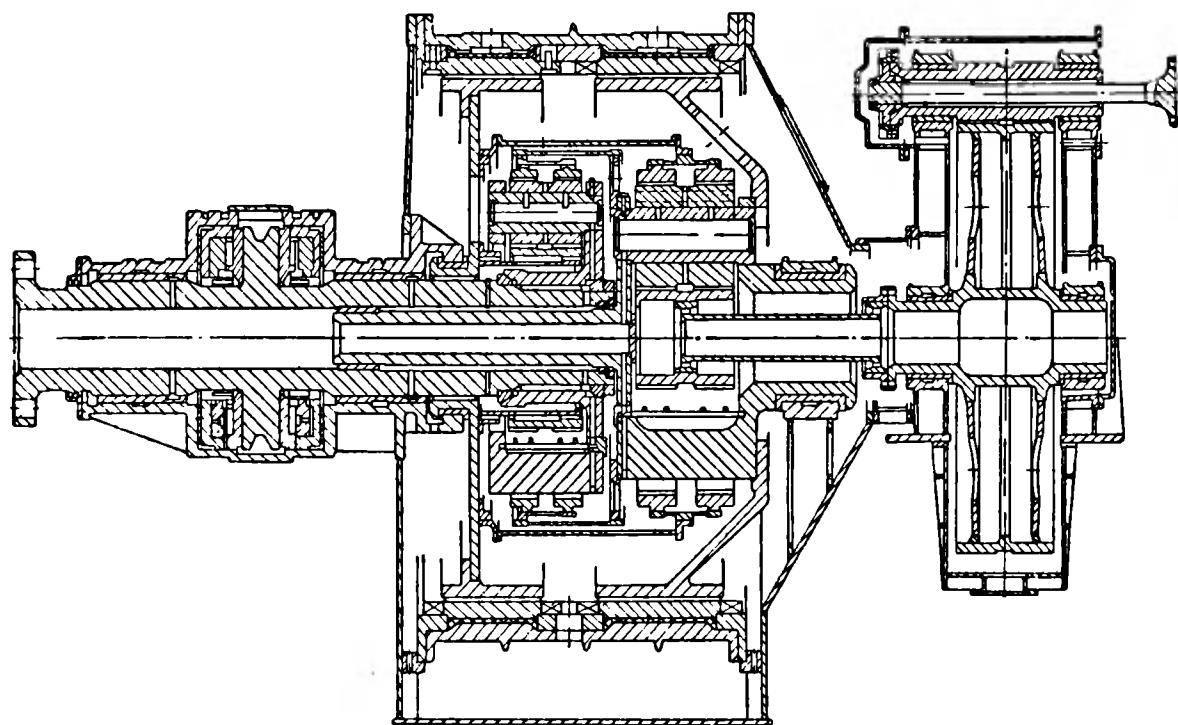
Продольное сечение реверсивного планетарного редуктора мощностью 13 000 л. с. (частота вращения: двигателя 4800 об/мин, гребного вала 100 об/мин на переднем ходу и 76 об/мин — на заднем).
